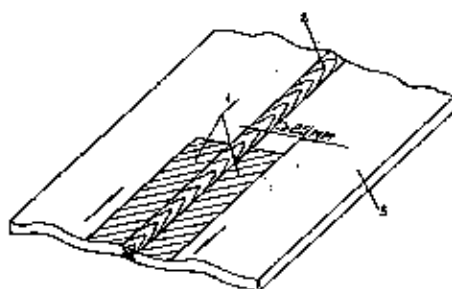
Схема упрочнения стыковых сварных швов:
